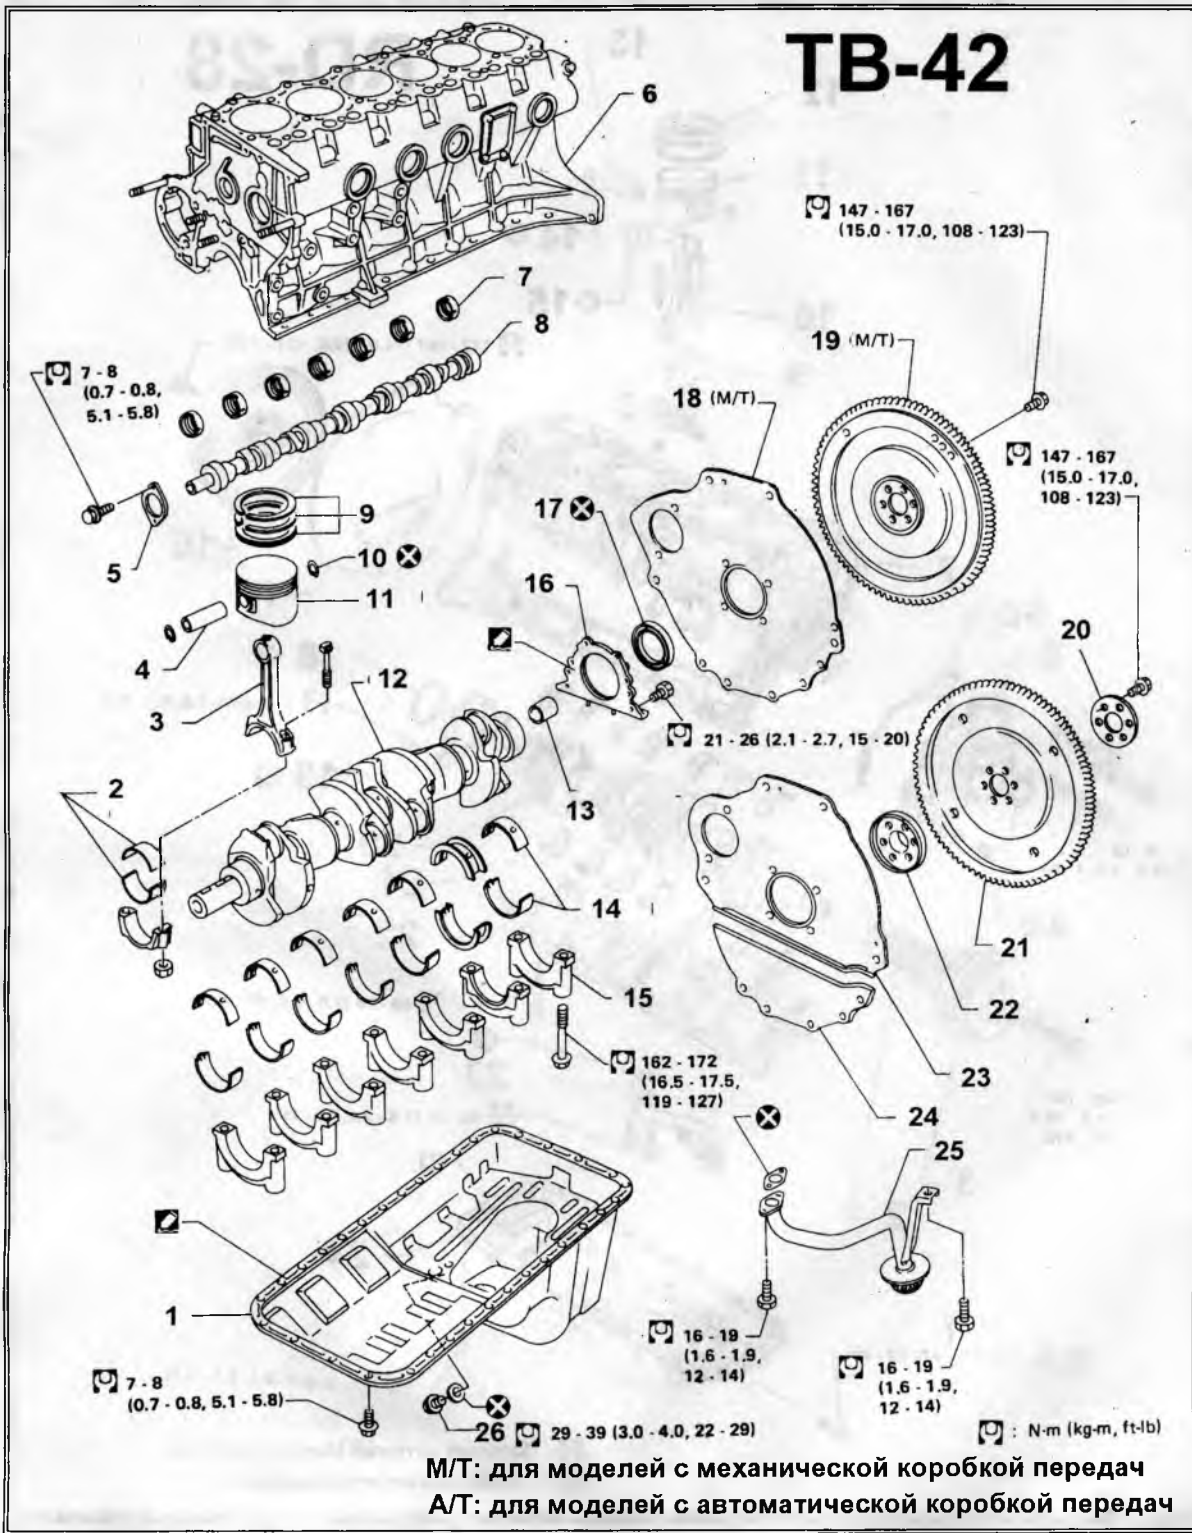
1. Поддон картера. 2. Вкладыши шатунных подшипников. 3. Шатун. 4. Поршневой палец. 5. Фиксатор положения распределительного вала. 6. Блок цилиндров. 7. Вкладыши распредвала. 8. Распредвал. 9. Поршневые кольца. 10. Стопорное кольцо. 11. Поршень. 12. Коленчатый вал. 13. Направляющая втулка. 14. Вкладыши коренных подшипников. 15. Крышки коренных подшипников. 16. Держатель заднего сальника коленвала. 17. Задний сальник коленвала. 18. Задняя плита. 19. Маховик. 20. Элемент крепления диска привода. 21. Диск привода. 22. Переходной элемент диска привода. 23. Задняя плита. 24. Пылезащитная крышка. 25. Маслоприемник. 26. Сливная пробка.
